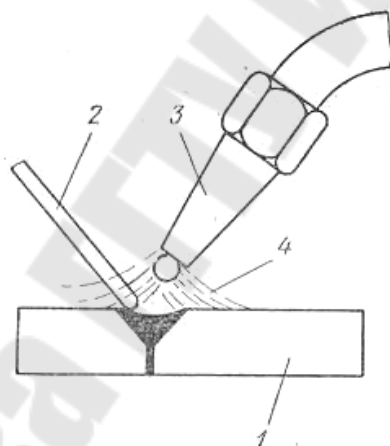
Схема газовой сварки: 1 – свариваемый материал; 2 – присадочный пруток; 3 – наконечник газовой горелки; 4 – газое пламя
